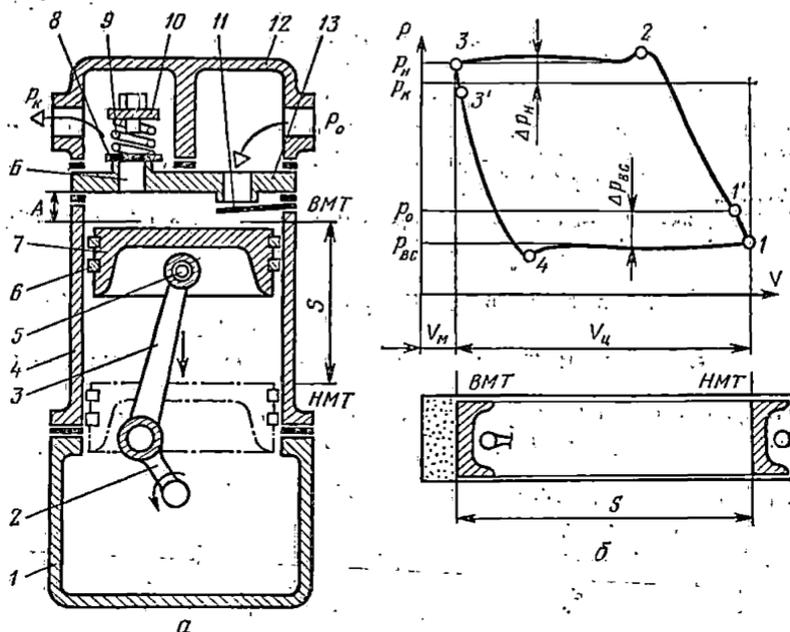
Принцип работы поршневого компрессора: а — схема компрессора; б — индикаторная диаграмма
